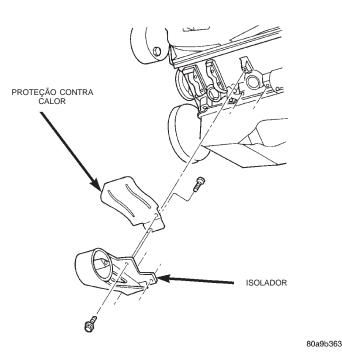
Montagem do Isolador Dianteiro do Lado Esquerdo do Motor — Veículos 2WD (Com Tração em 2 Rodas)
